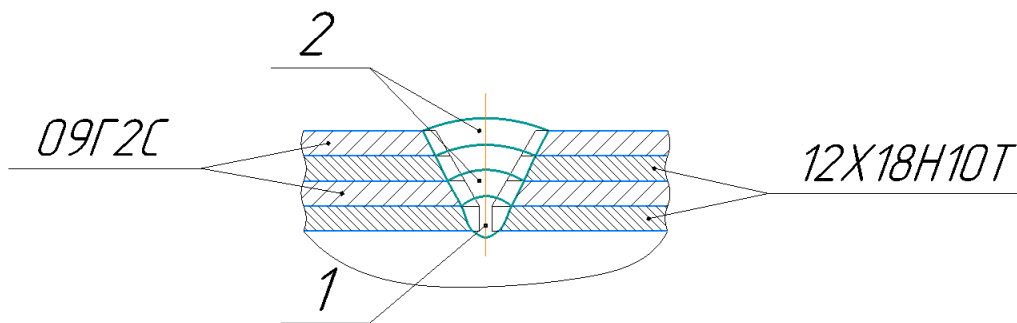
Пример одностороннего V-образного сварного соединения труб из 4-х слойного металлического материала с внутренним протектором и порядок наложения швов: 1 – корневой проход; 2 – заполняющие проходы
